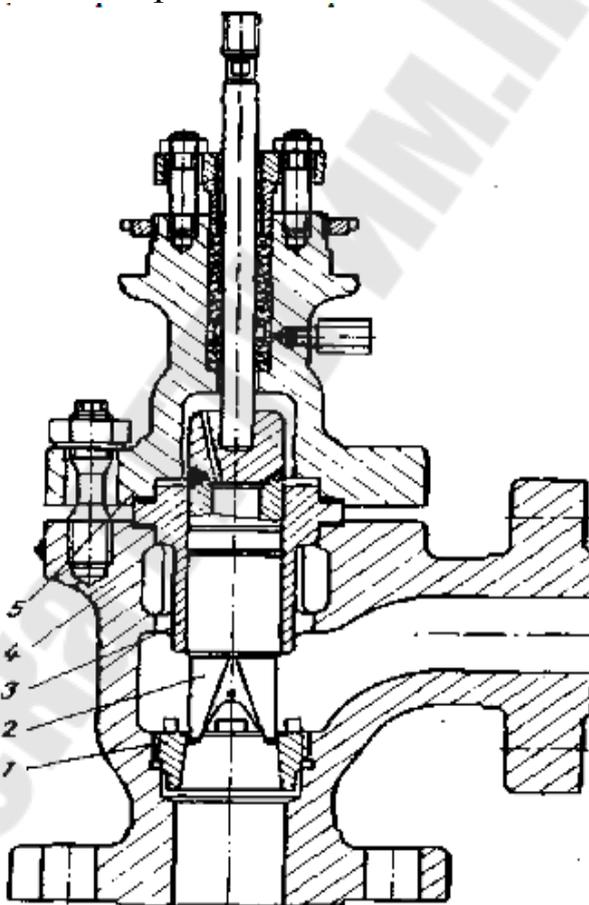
Регулирующий орган односедельного клапана с разгруженным затвором: 1 – седло; 2 – затвор; 3 – направляющая втулка; 4 – корпус; 5 – верхняя крышка.
